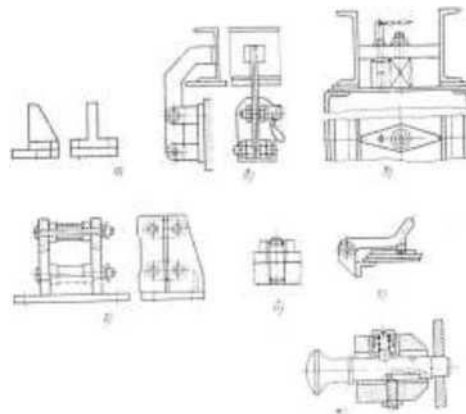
Установочные элементы сборочных приспособлений:
